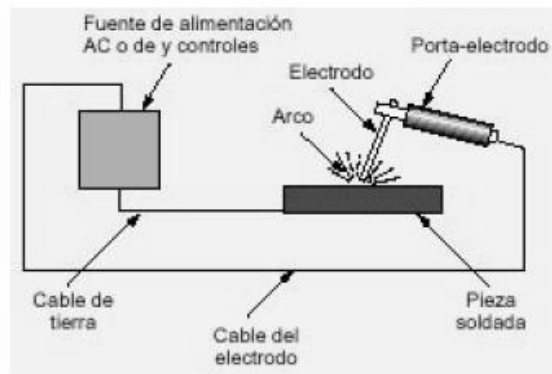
Esquema del proceso de soldadura eléctrica al arco
